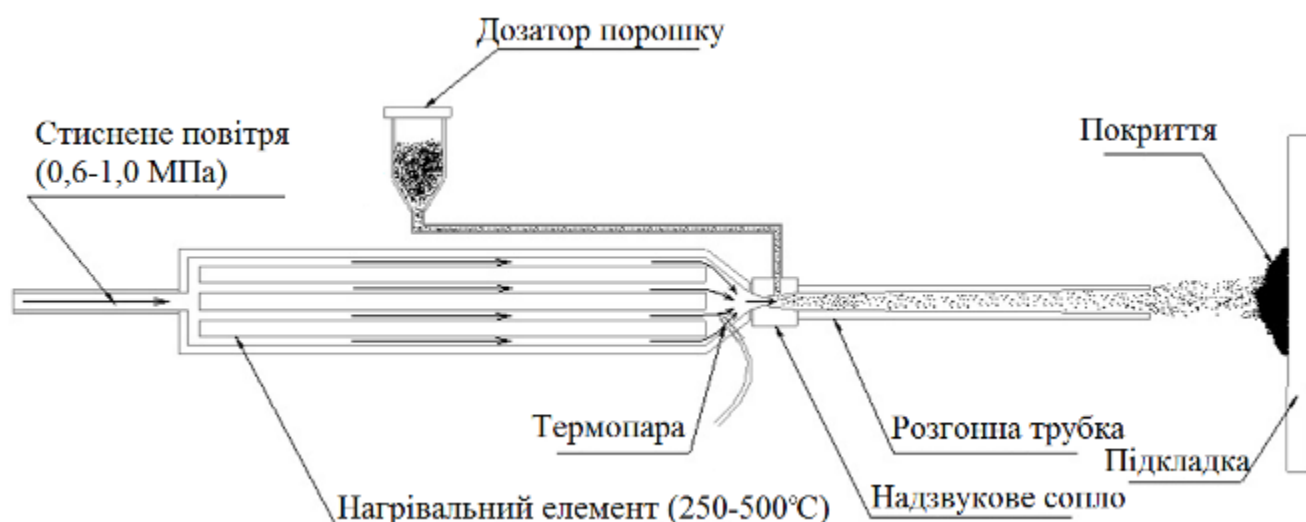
Схема установки для холодного газодинамічного напилення
